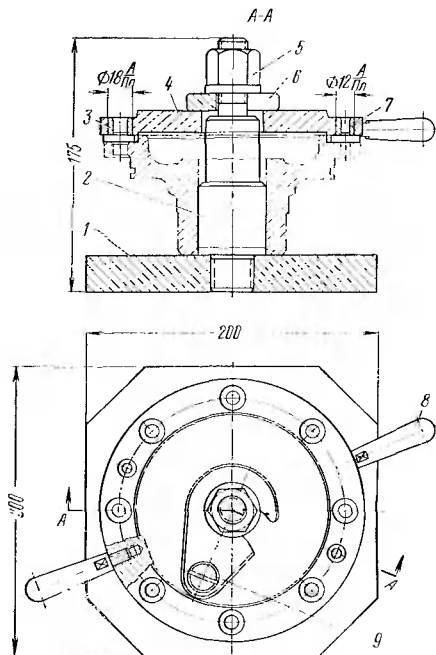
Кондуктор для сверления отверстий во фланце вала ведущей шестерни заднего моста:
